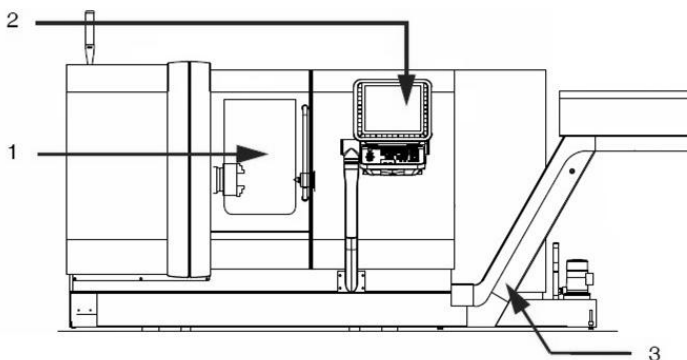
Внешний вид токарного станка с ЧПУ СТХ alpha 500:
